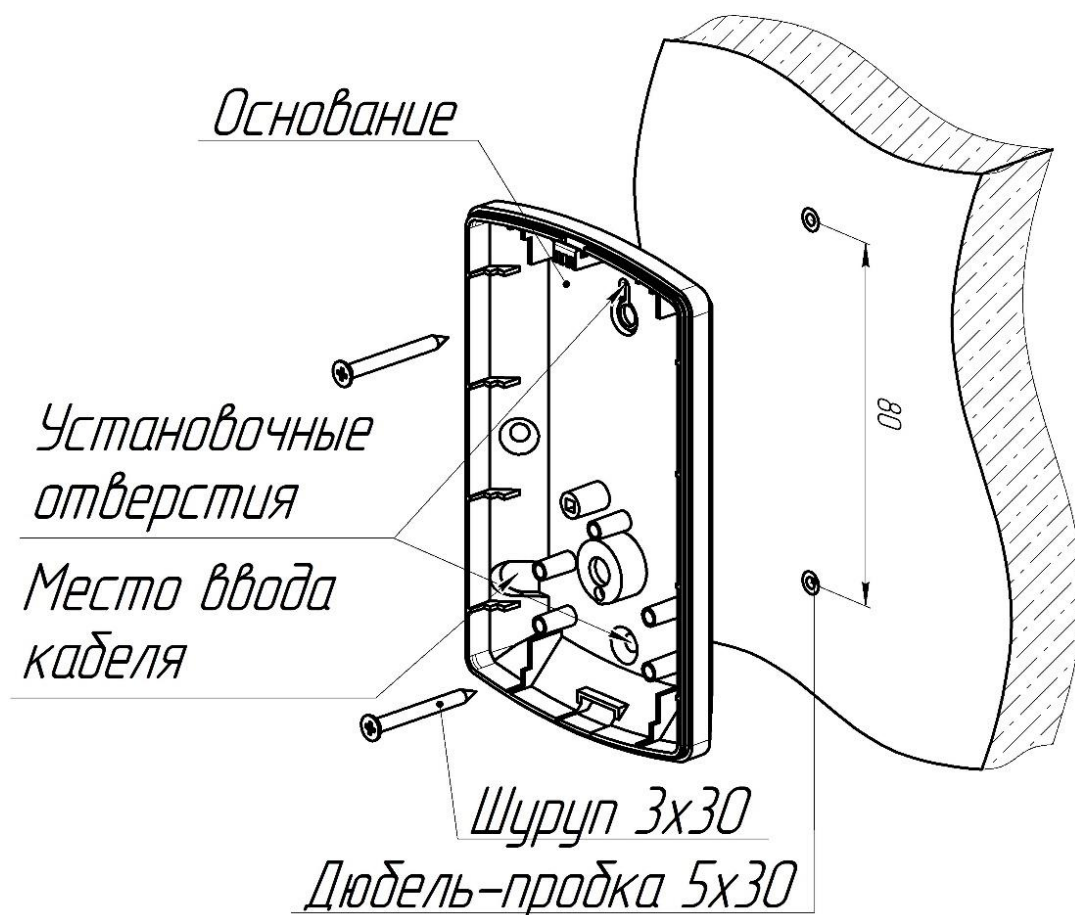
Крепление извещателя на стену без кронштейна
